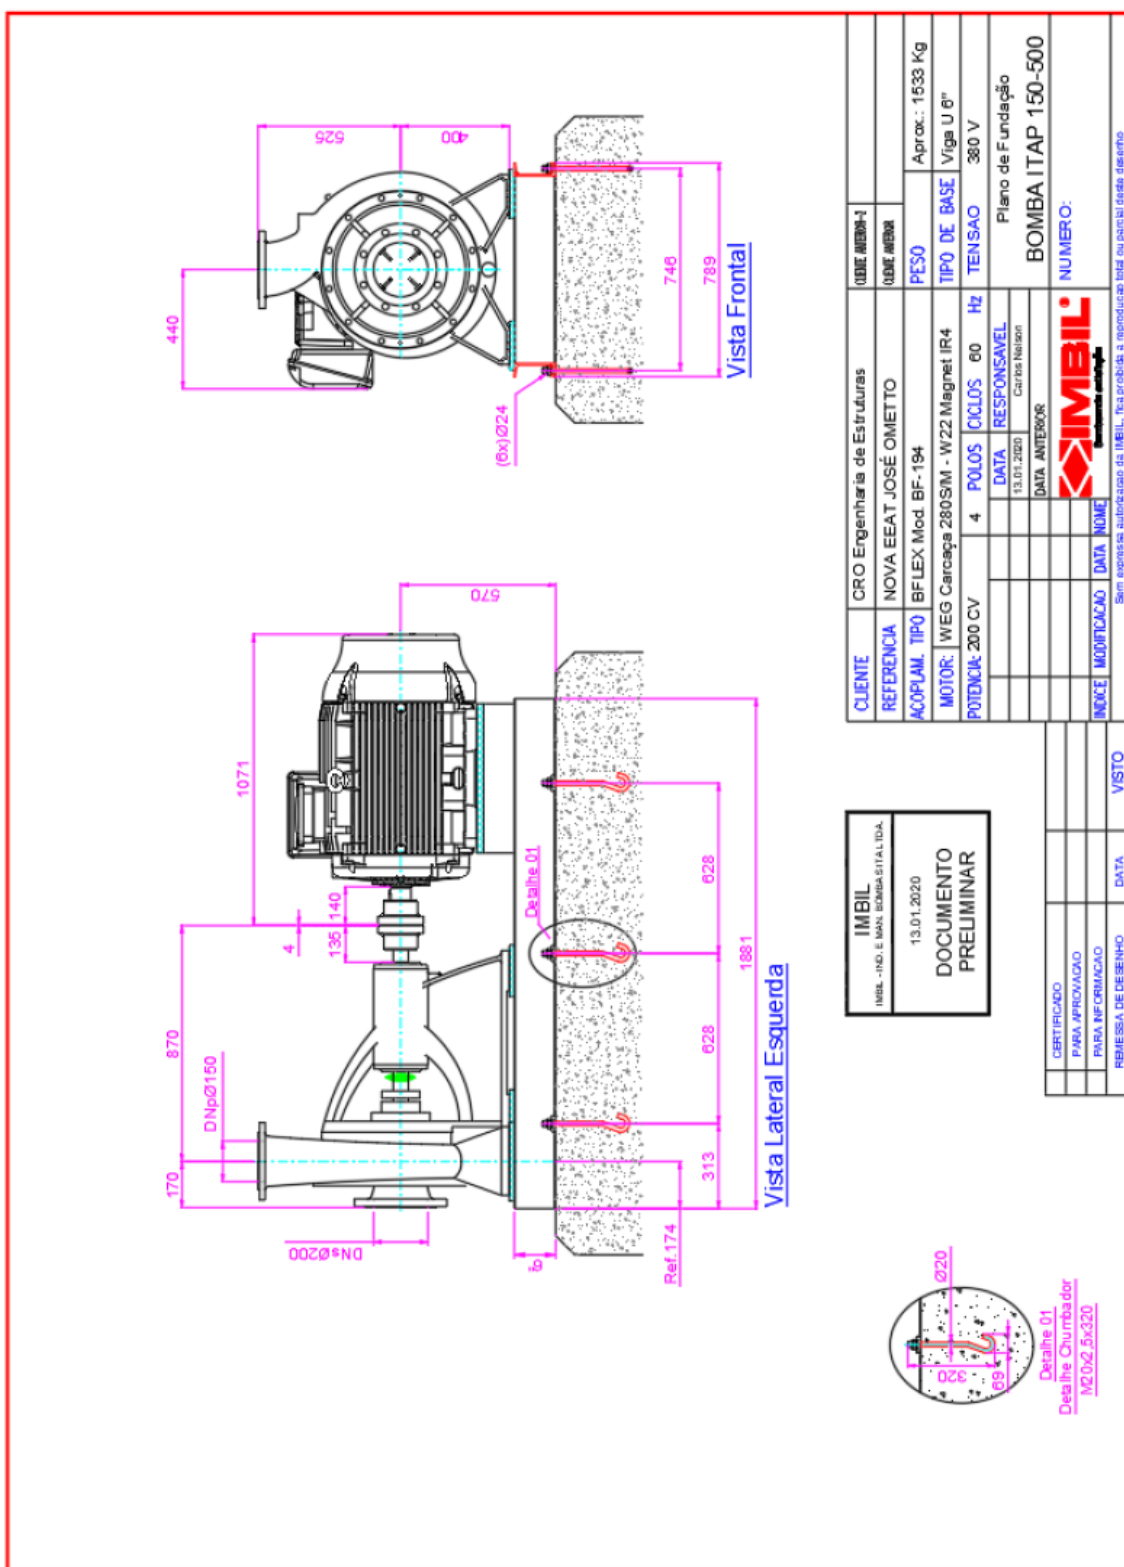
Imagem X: Dimensional do Conjunto Motobomba Selecionado
